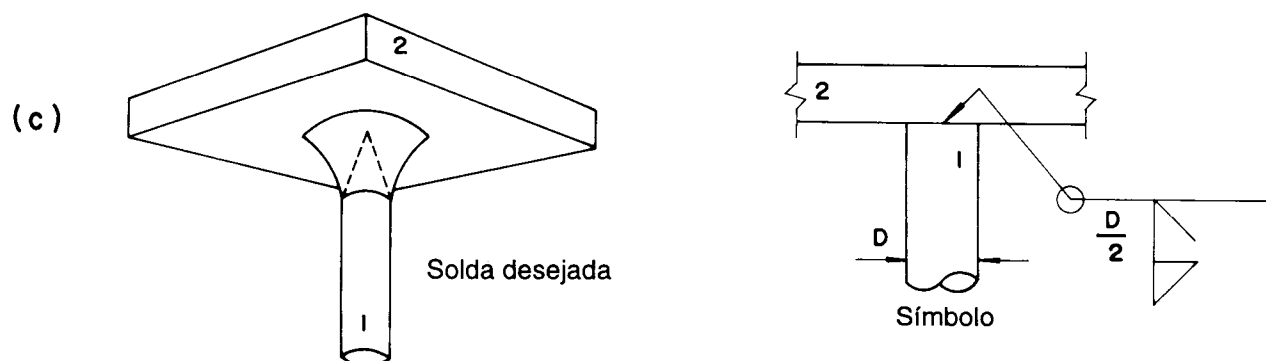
Exemplos de símbolos de acabamento de soldas
